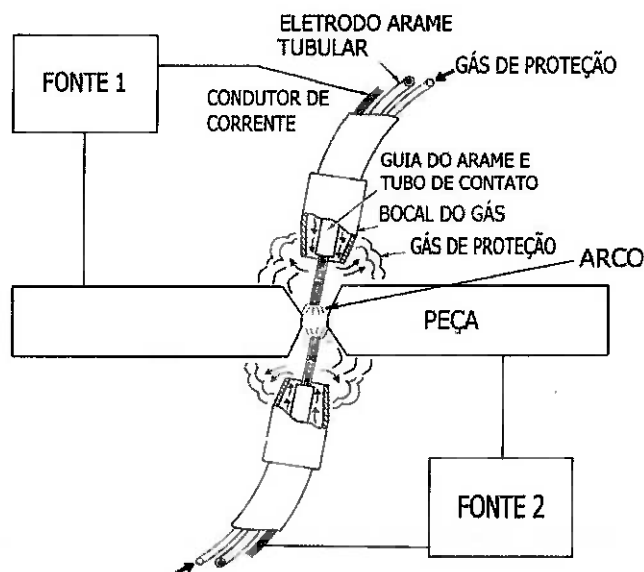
Esquema para a soldagem Dupla Fusão e Soldagem a Plasma. Alumínio 5052 (Modificado de [12]).
